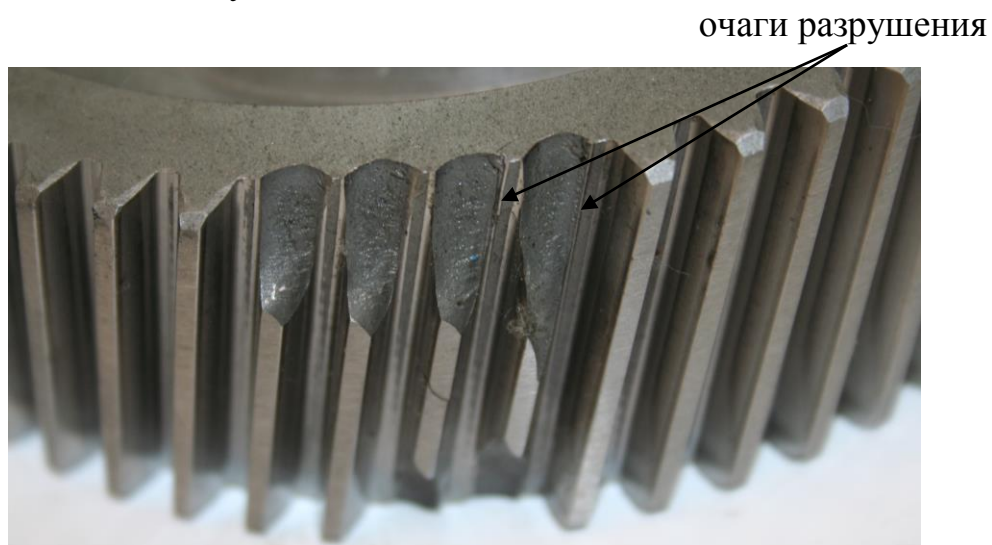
Поверхности излома зубьев разрушенной детали.
